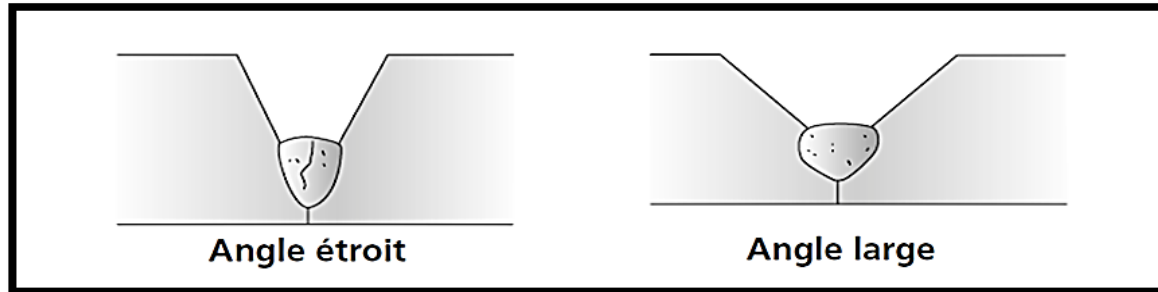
Préparation d'un joint pour la prévention de la fissuration à chaud [23]
